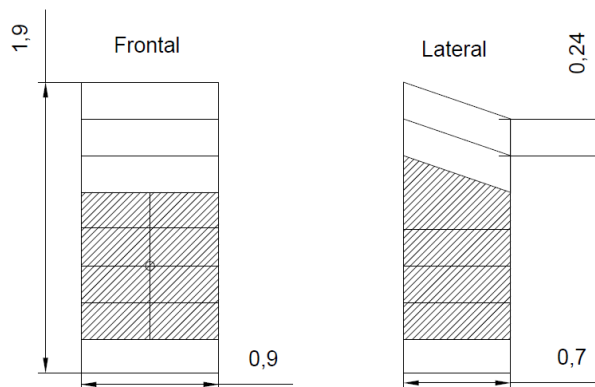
Esboço do armário/estante para o subposto paralelo.
